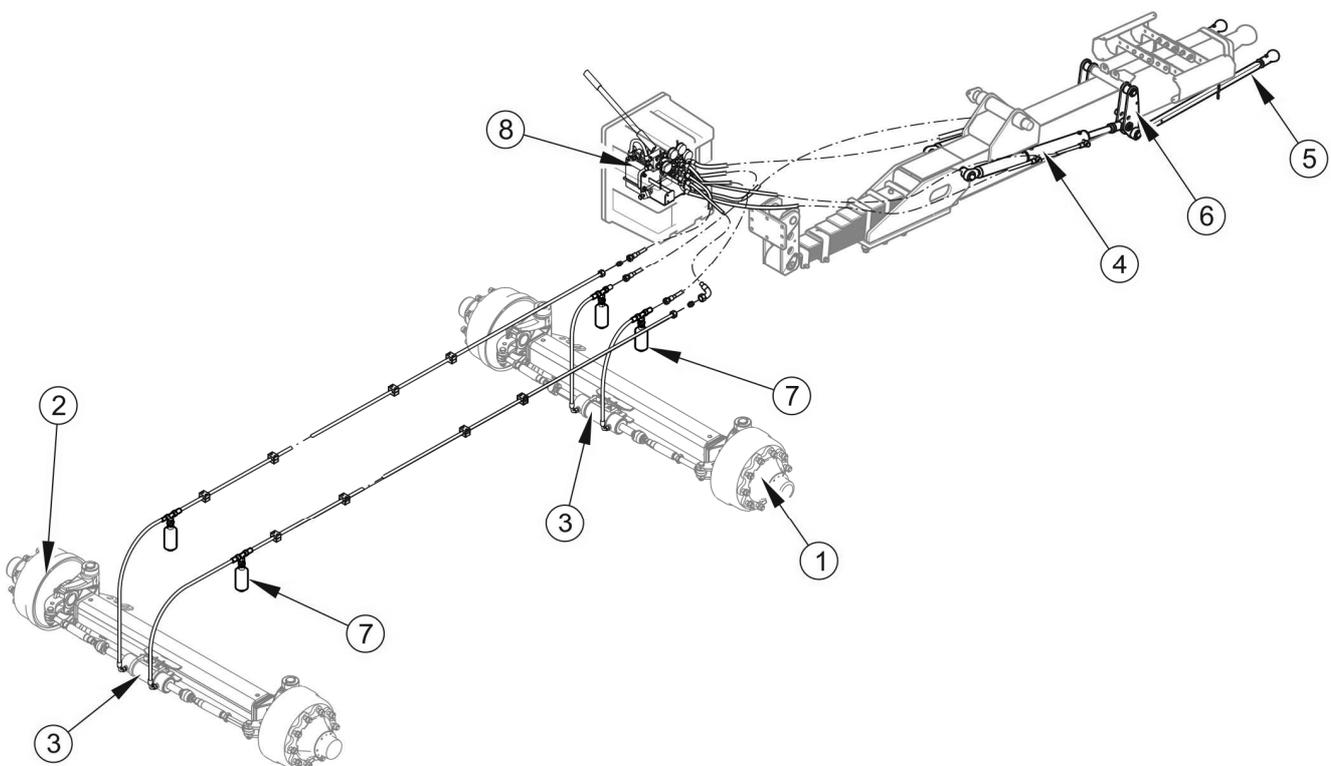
Costruzione e schema dell'impianto idraulico dello sportello
